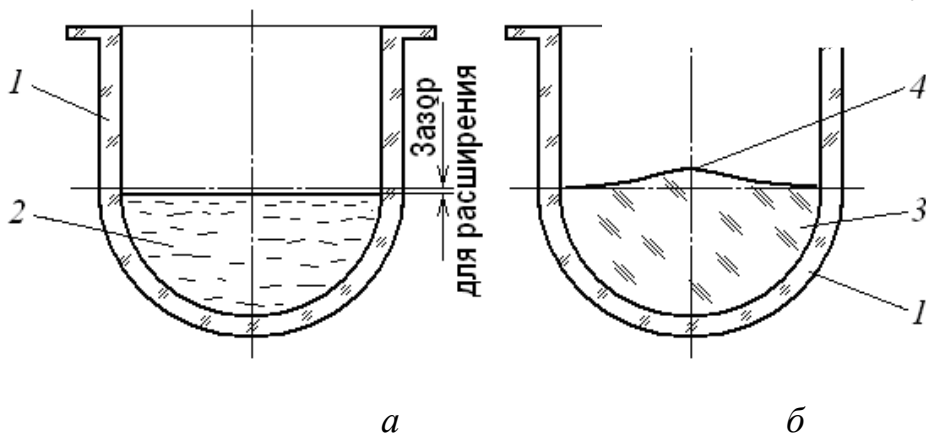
Внешний вид и форма колпачков для изготовления ледяных полусфер
